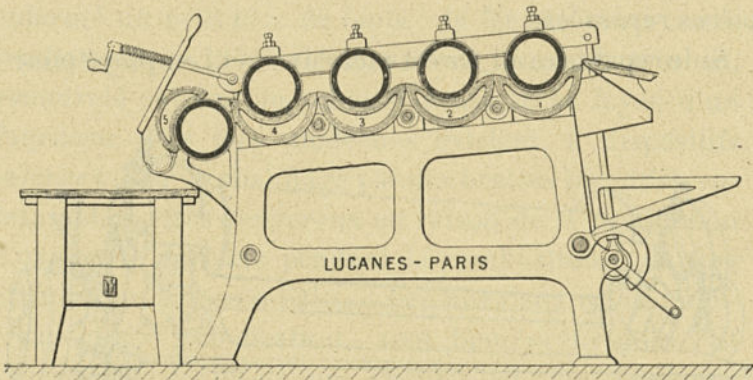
Coupe d'une machine à cuvettes (Lucanes).
